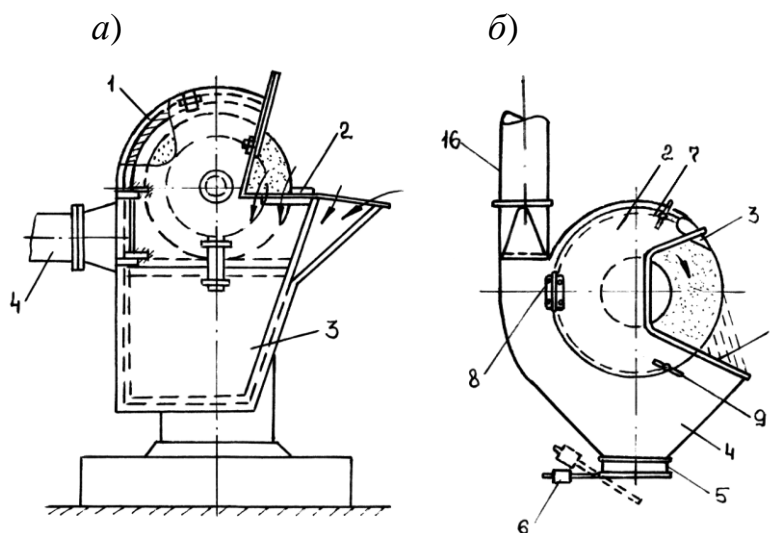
Кожухи-пылеприёмники: *а* – для заточного станка; *б* – для шлифовального или полировального кругов.
